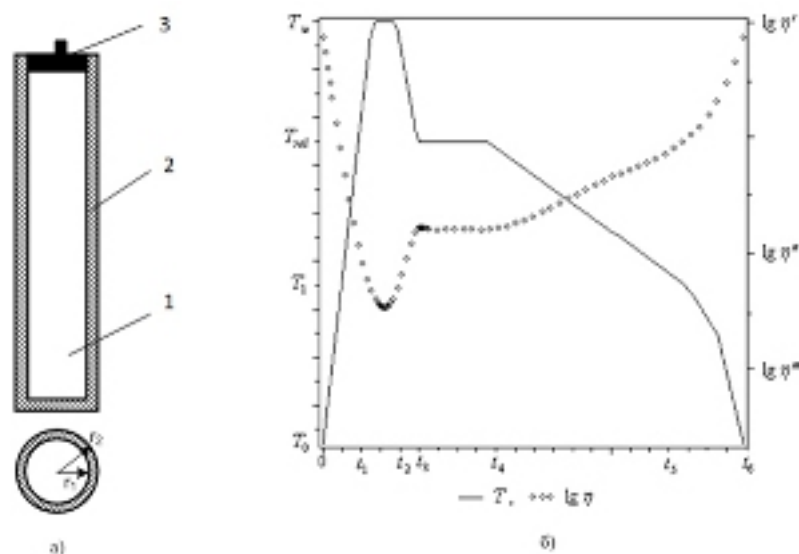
а) схематическое изображение сборки: 1— стеклянный стержень, 2— внешний металлический стакан, 3— внутренний металлический стакан, 4— подвижная крышка; б) температурный режим сварки:  $T$ — температура сварки,  $\lg \eta$ — логарифм динамической вязкости стекла.
